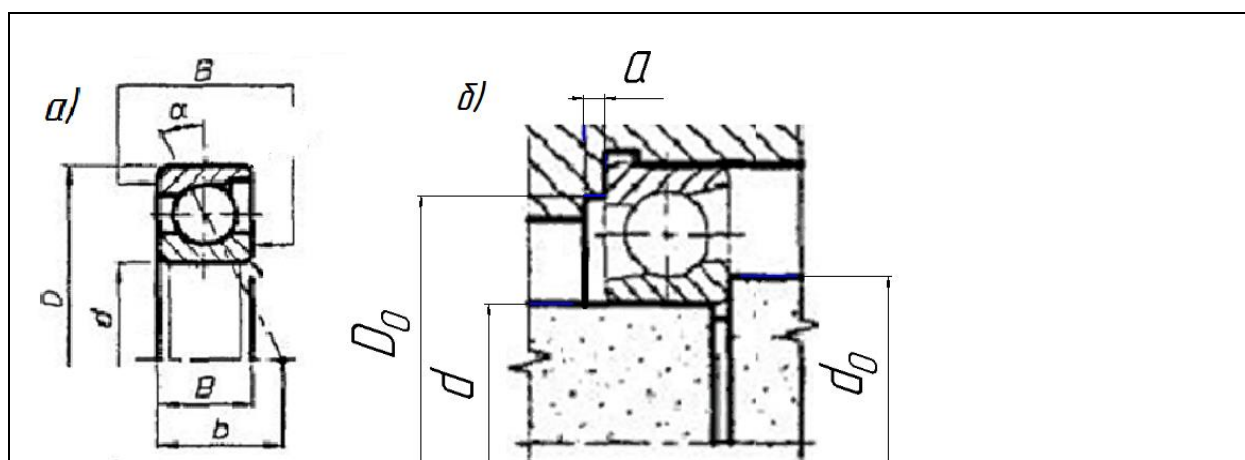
Размеры подшипника (а) и упорных буртиков вала и корпуса (б)
